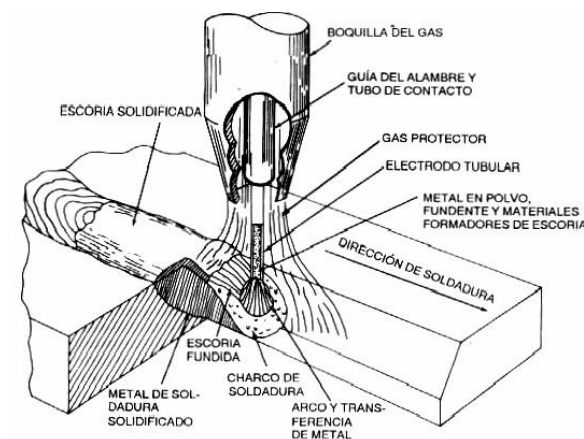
Diagrama de soldadura de pieza metálica
